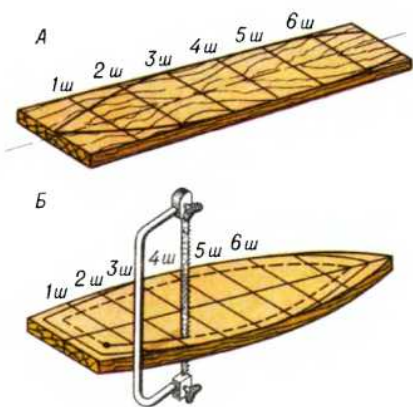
Подготовка досок для корпуса модели: А — разметка досок; Б — обработка снаружи и выпиливание изнутри.
